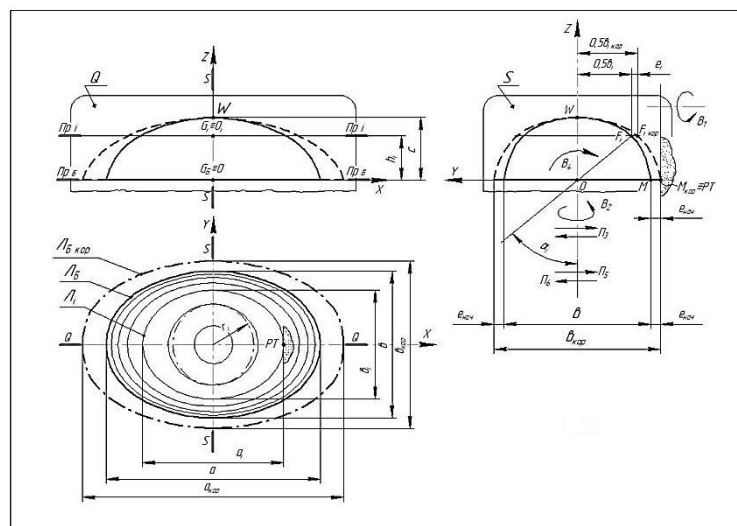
Кабошон с овальным базовым профилем и схема движений при его формообразовании
